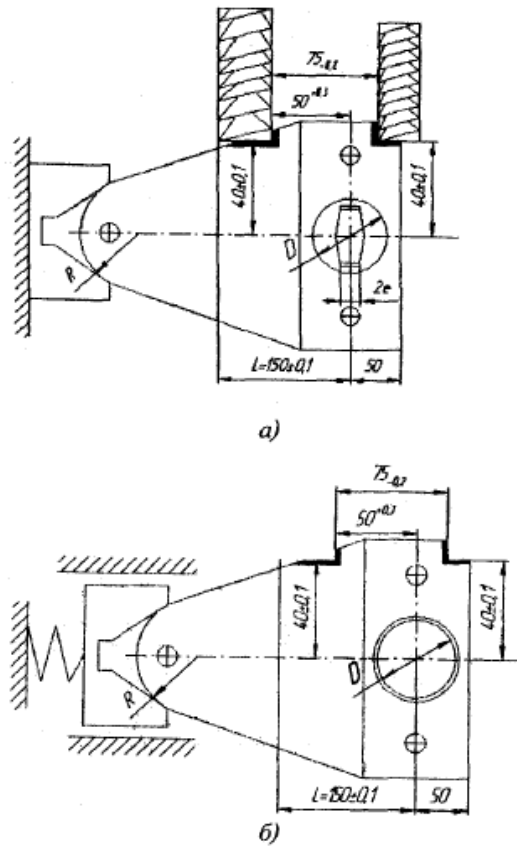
Схема установки заготовки на центруючий штифт і призму
